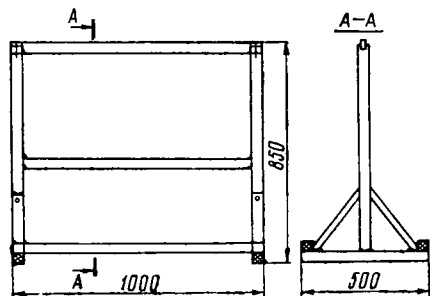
Эскиз стойки для сварки пленки в полотнище
